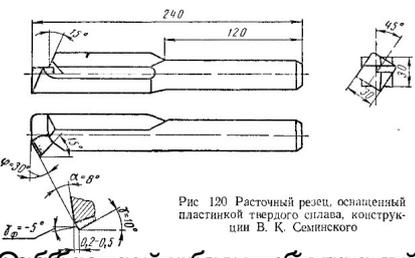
Расточный резец, оснащенный пластинкой твердого сплава, конструкции В. К. Семянского
